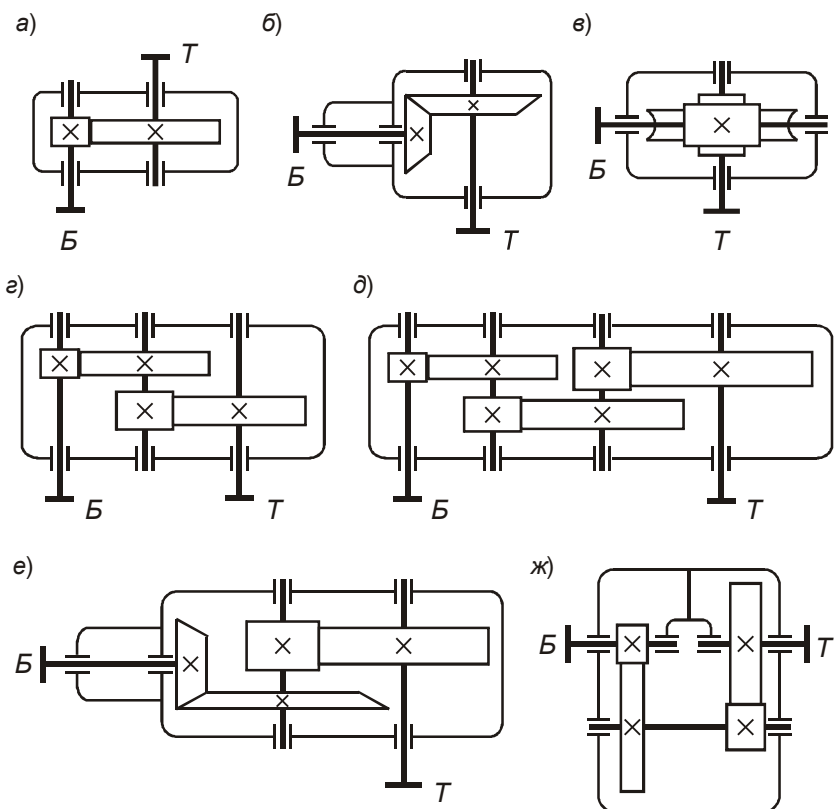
Схемы редукторов: а – цилиндрический одноступенчатый; б – конический одноступенчатый; в – червячный одноступенчатый; г – цилиндрический двухступенчатый развернутой схемы; д – цилиндрический трехступенчатый развернутой схемы; е – коническо-цилиндрический двухступенчатый; ж – соосный двухступенчатый
